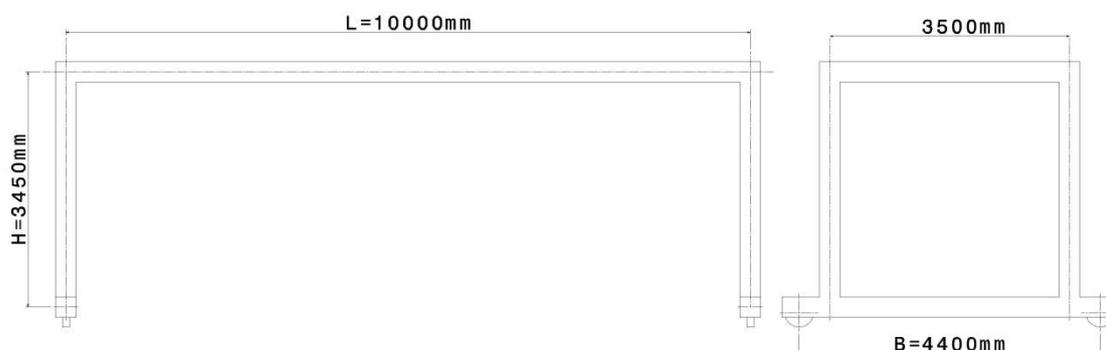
Esquema geral do pórtico de soldadura
